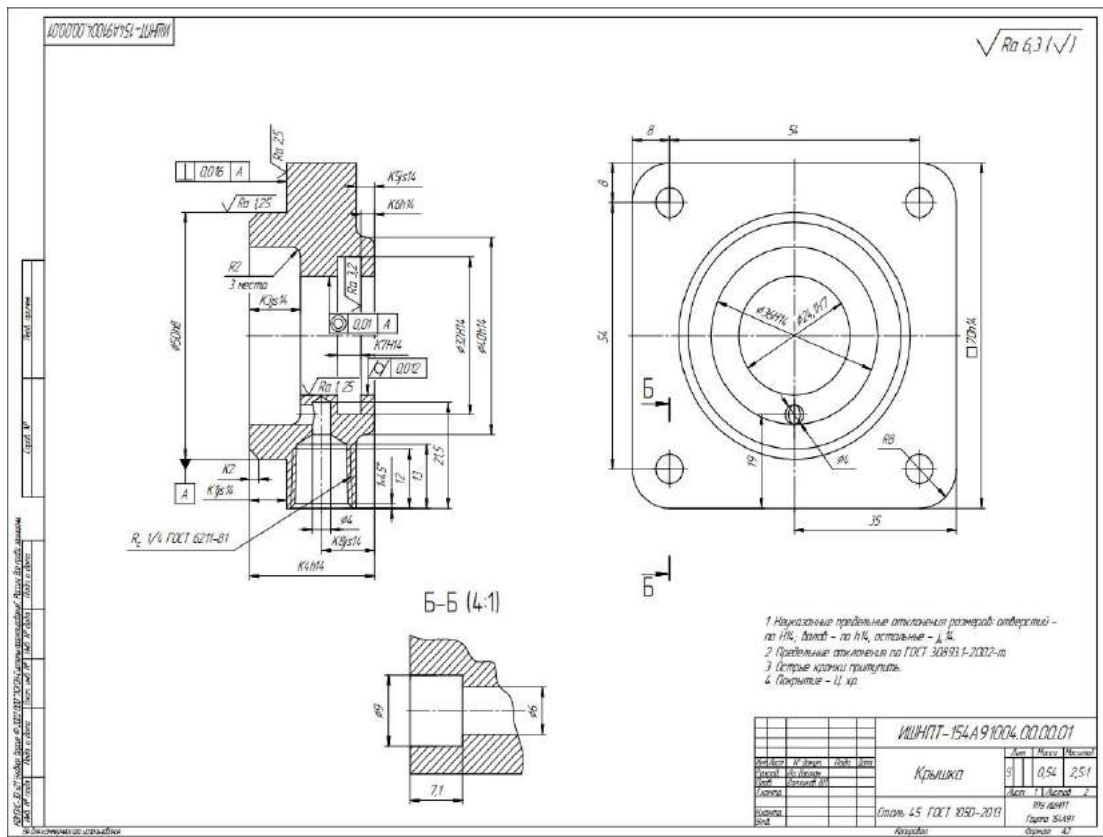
Эскиз детали для проверки учёта всех конструкторских размеров в комплексной схеме обработки детали в осевом направлении
